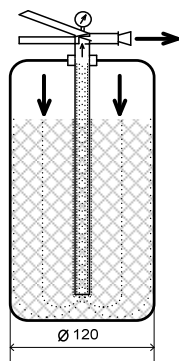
Общий вид конструкции порошкового огнетушителя
